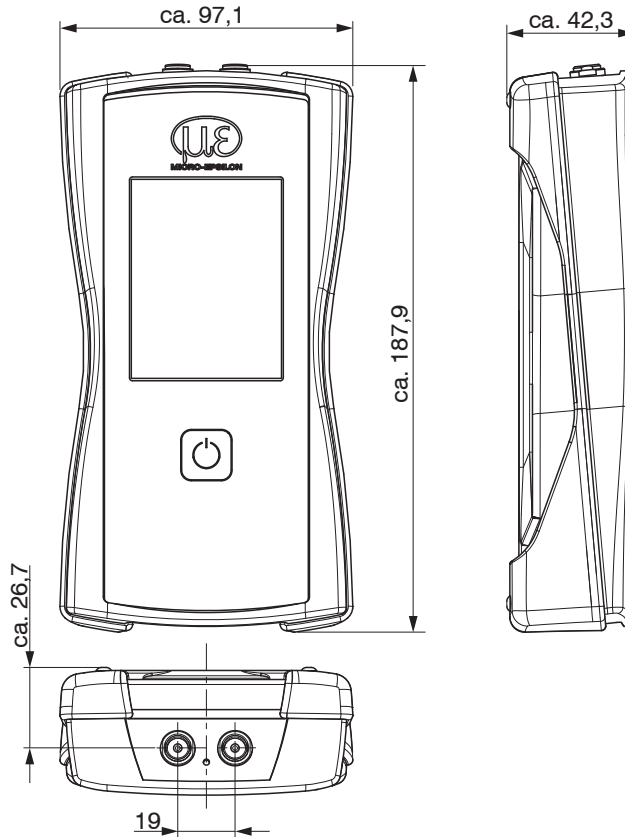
Maßzeichnung Controller, Abmessungen in mm, nicht maßstabsgetreu
